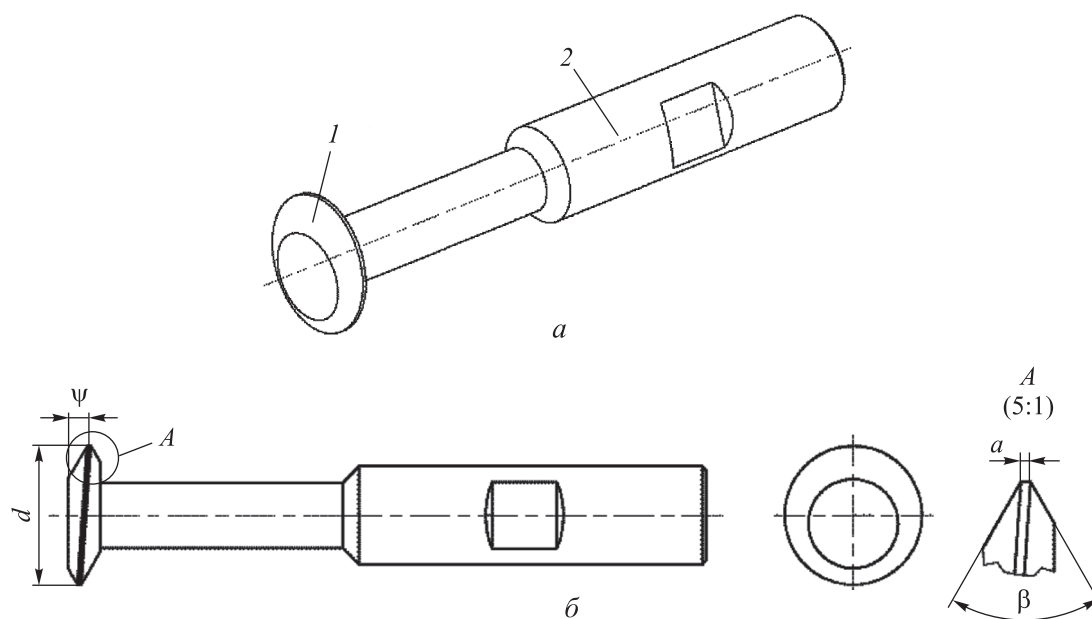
Конструктивные схемы неразъемного планетарного раскатника с одним ФОД
